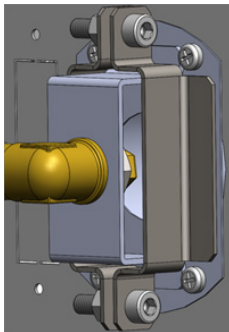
Die Luftabdeckung des Backofenbrenners (1-besteht aus zwei mit Schrauben zusammengeschraubten Blechen)
